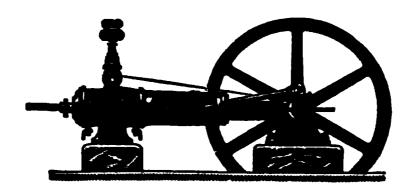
Maschinen mit Bajonettrahmen bis 800 Hub und hinten geführter Kolbenstange.
